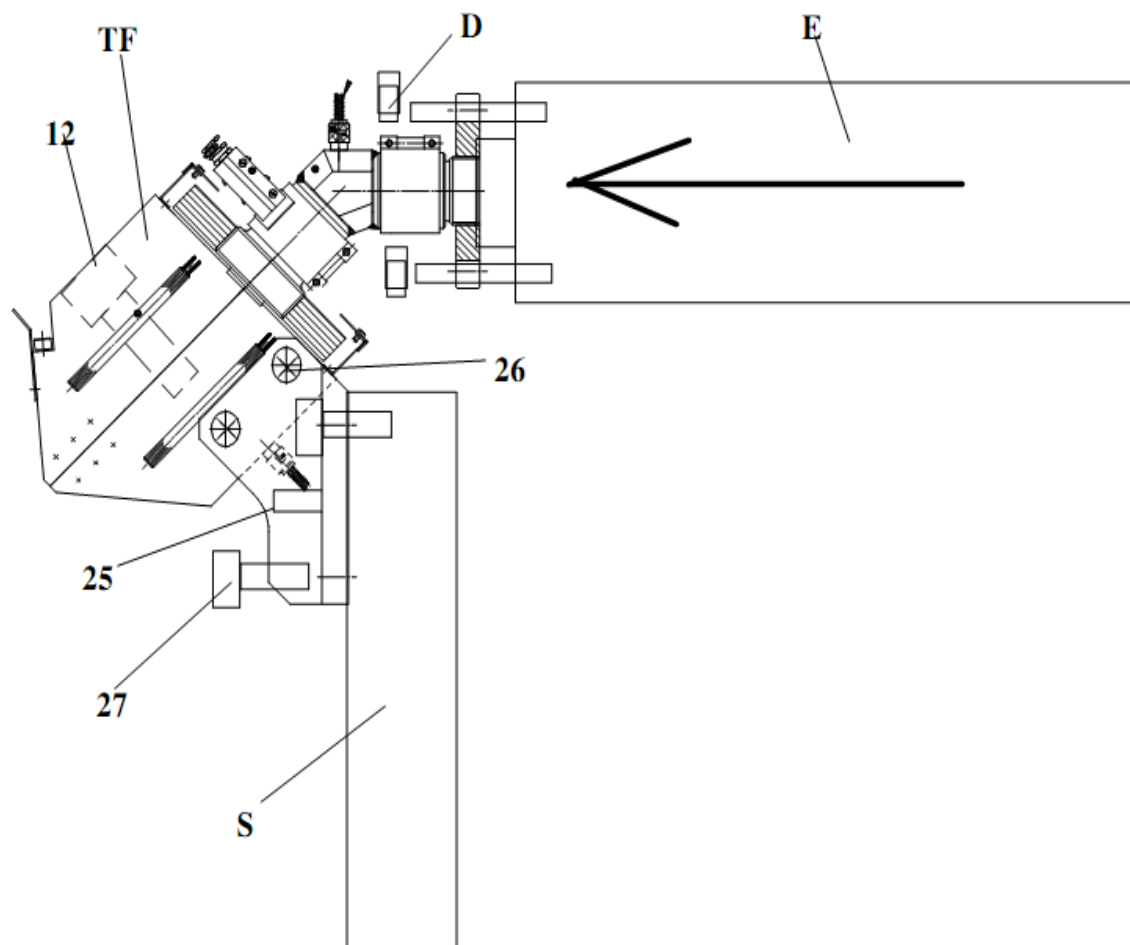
Rappresentazione del montaggio della testa all'estrusore (disegno rilasciato dall'AMUT S.p.A.).
